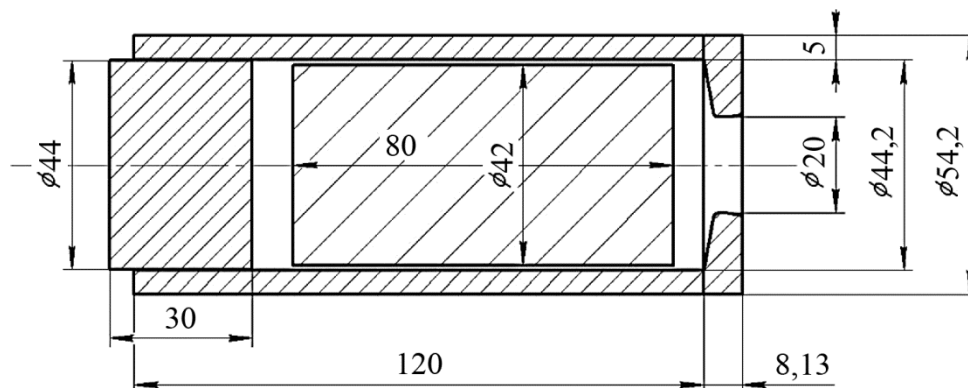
Размеры заготовки и оснастки для прессования в лабораторных условиях ИМАШ УрО РАН
